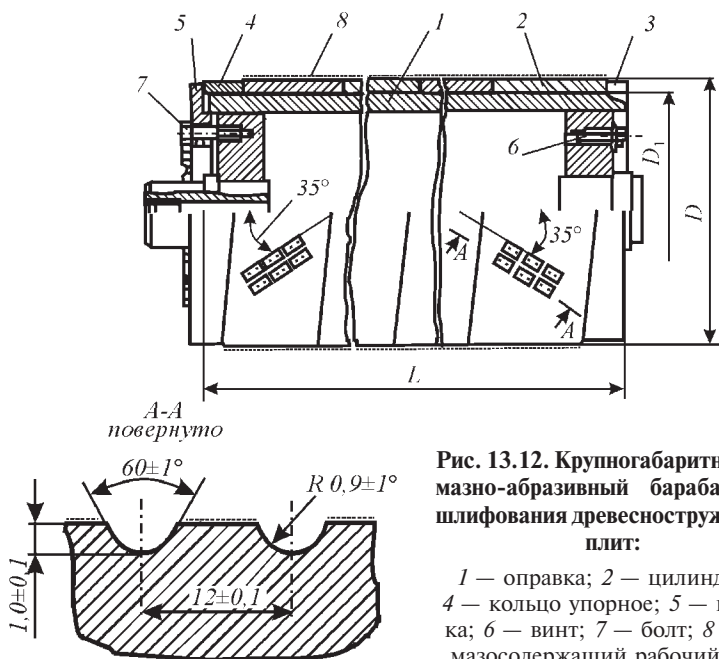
Крупногабаритный алмазно-абразивный барабан для шлифования древесностружечных плит:
